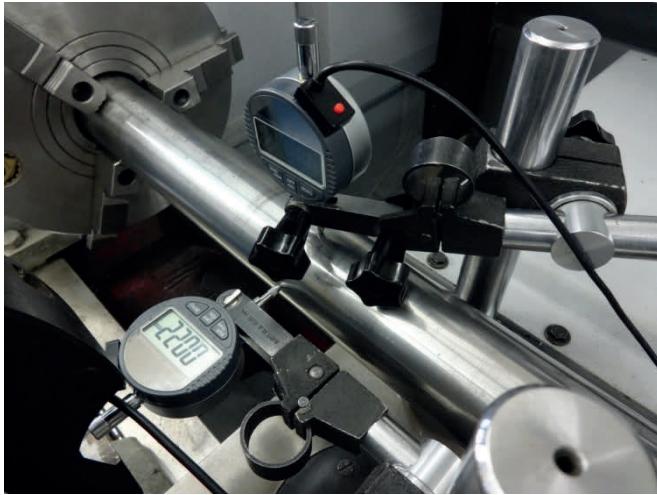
Фото установки для проверки токарного станка 16К20Ф3 на точность
